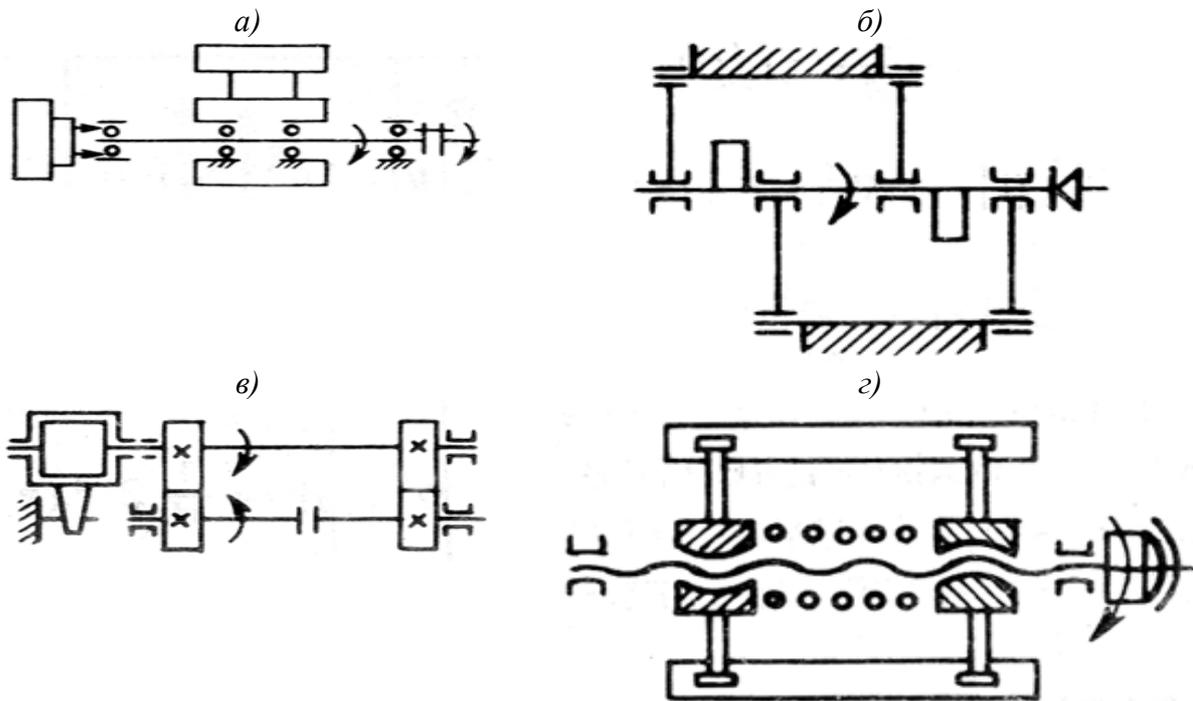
Схемы стендов для испытаний сборочных единиц (узлов):
